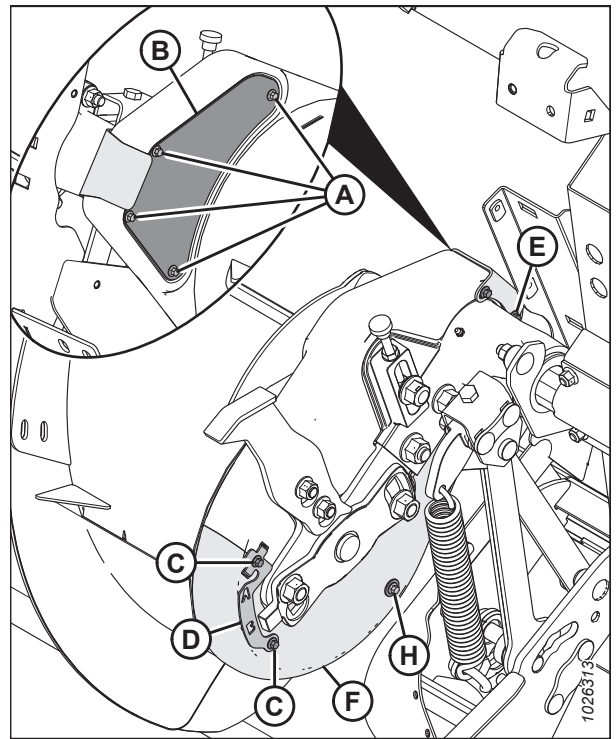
Einzugstrommelgetriebe – Rückansicht
